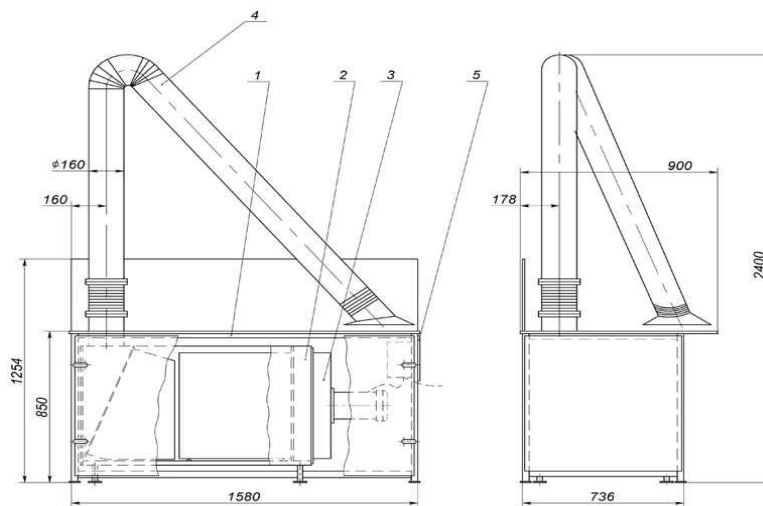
Схема стола сварщика. 1 - ПАР; 2 - стол сварочный; 3 - вентилятор с электродвигателем; 4 - консольно-поворотное устройство; 5 - блок управления
